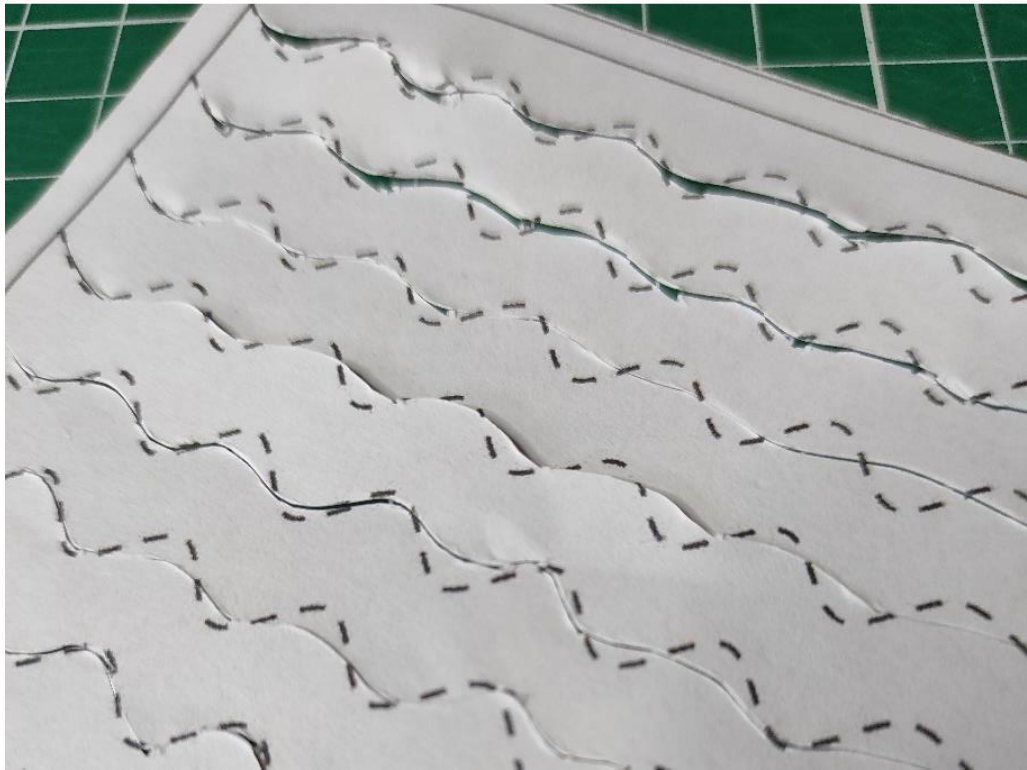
Patrón en ondas mal cortado por la cuchilla plana.
